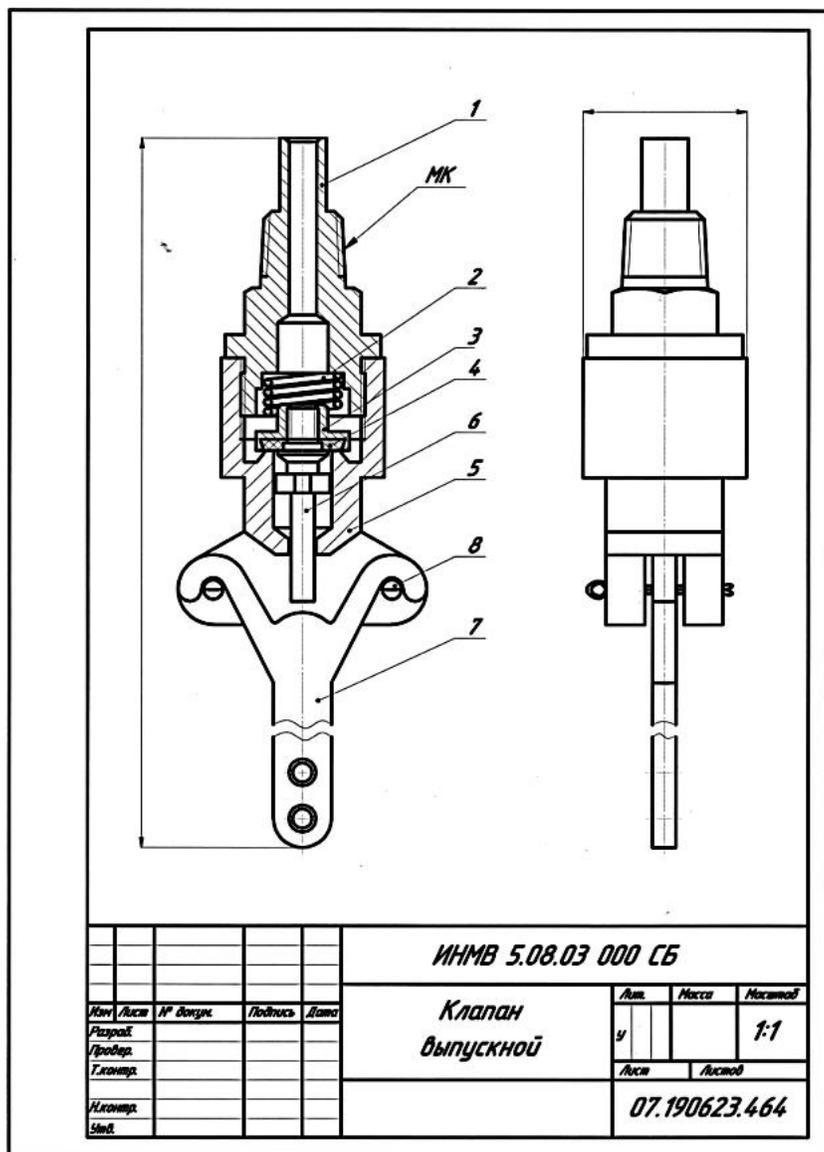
Образец сборочного чертежа для самостоятельной работы № 6 (вариант 3)
